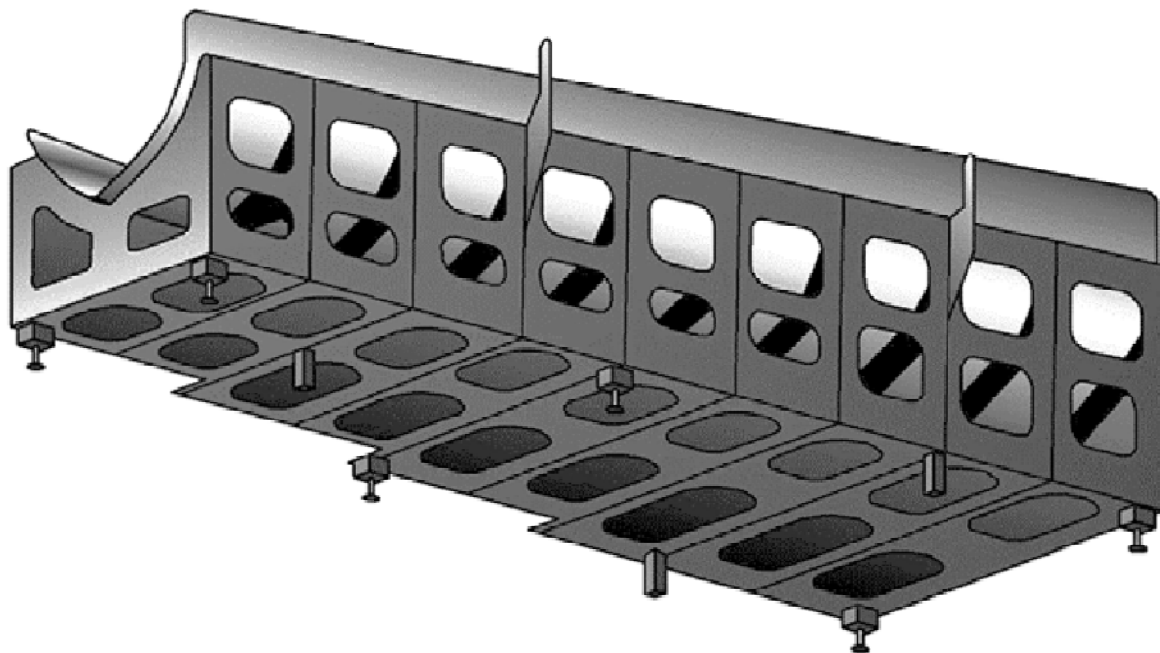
Схема автоклавной оснастки для инфузионной горячей формовки деталей из КМ
